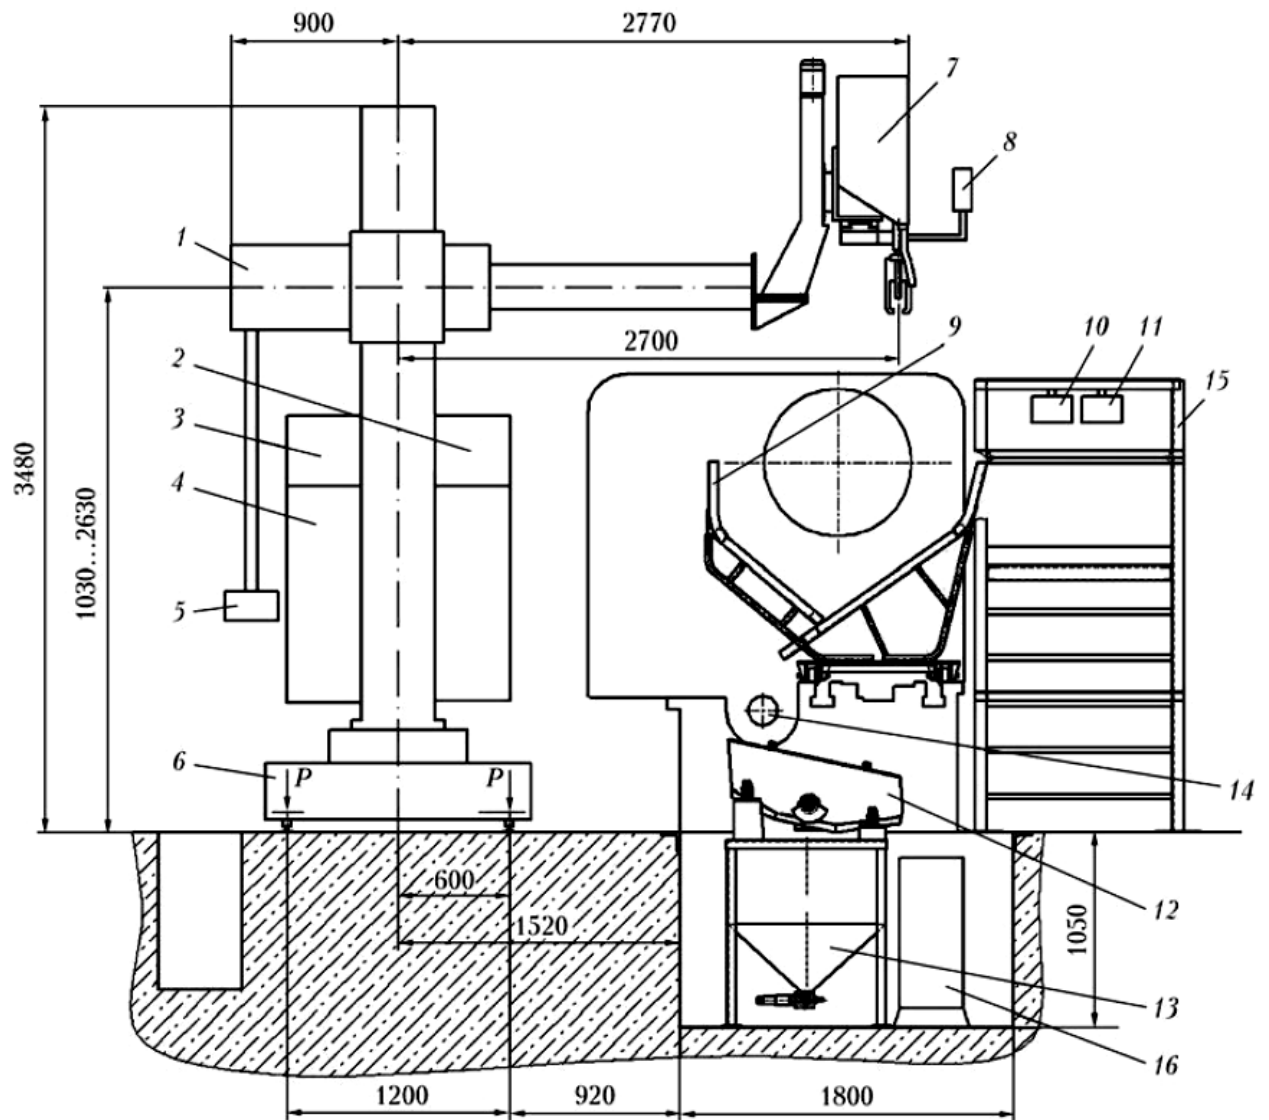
Схема установки для наплавлення прокатних валків заготівельних станів
